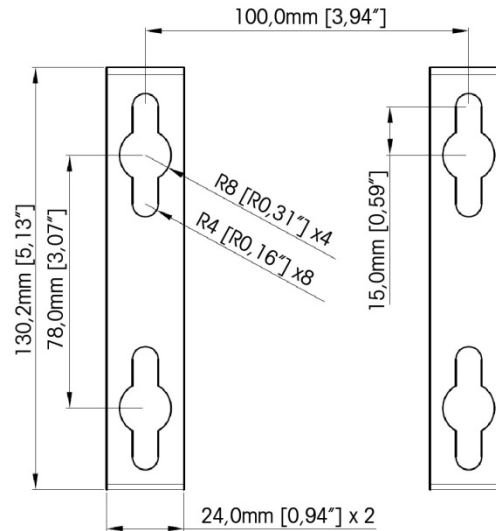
Patrón de orificios para montaje del soporte en la pared (VESA 100 x 100mm) (En terminales IND570 fabricados hasta abril de 2016)
